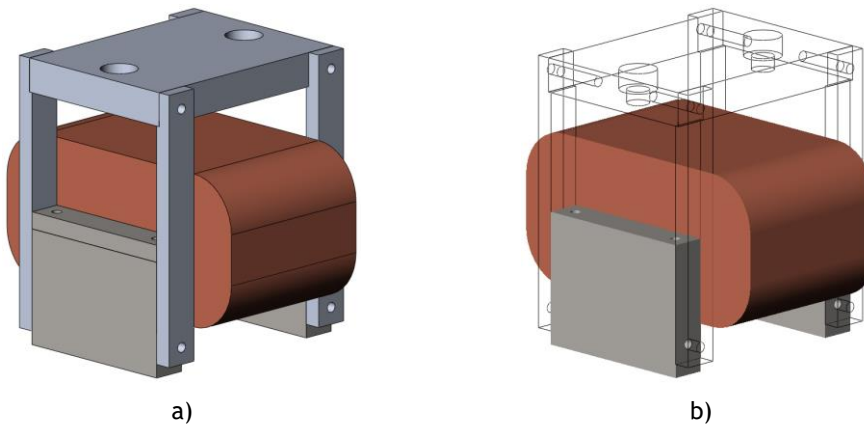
Subconjunto de montagem das fases do actuador: a) montagem completa e b) vista parcial em estrutura de arame e detalhe dos elementos do circuito magnético: bobina, núcleo e pólos.
